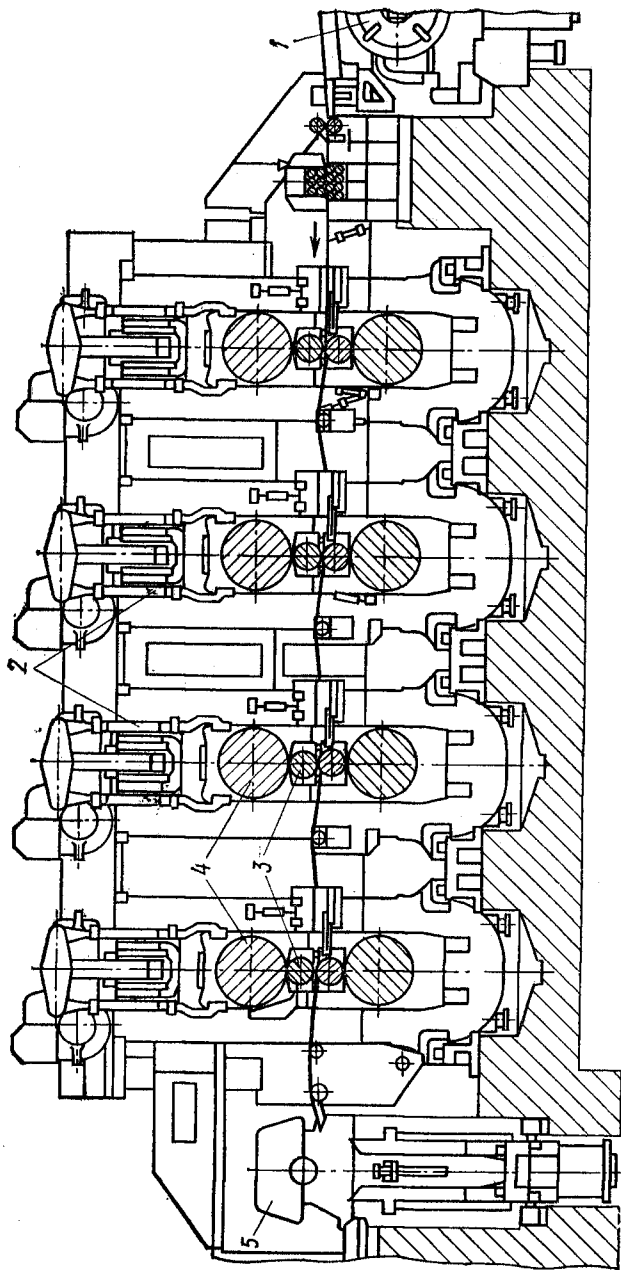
Схема непрерывного четырехклетьевого стана для холодной прокатки:
